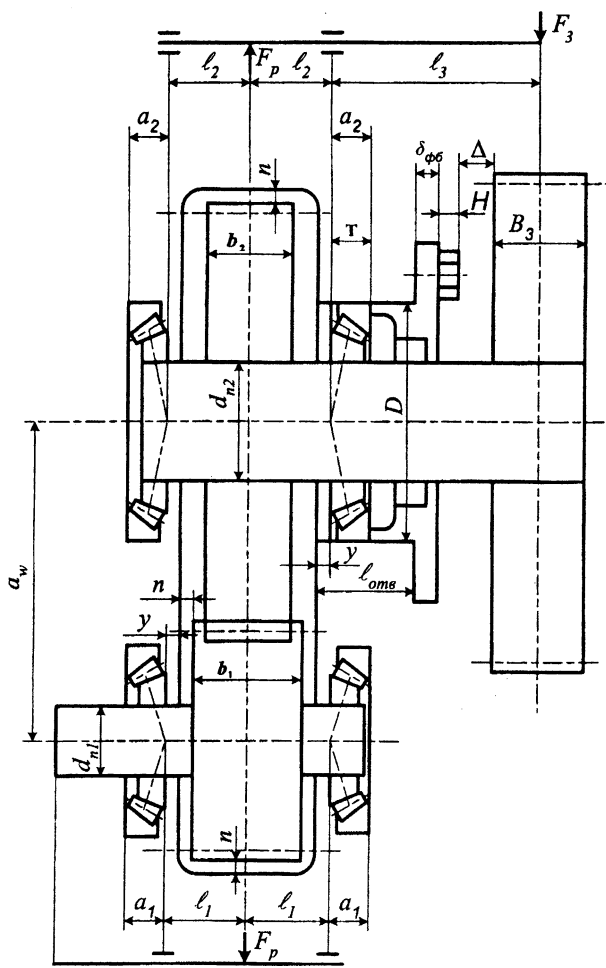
Эскизная компоновка цилиндрического редуктора с условно изображенными нагрузками на схемах валов
